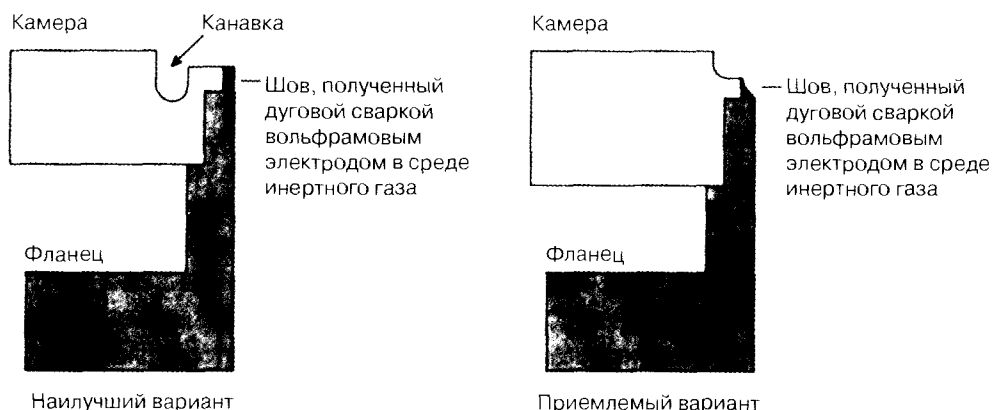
Рекомендуемая конструкция сварных соединений для алюминиевых фланцев
